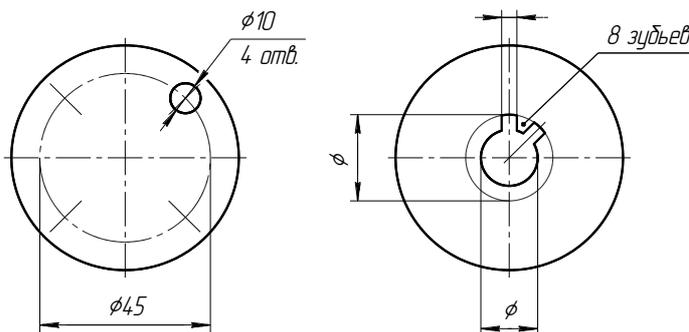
Условный показ отверстий и зубьев равномерно расположенных на детали
